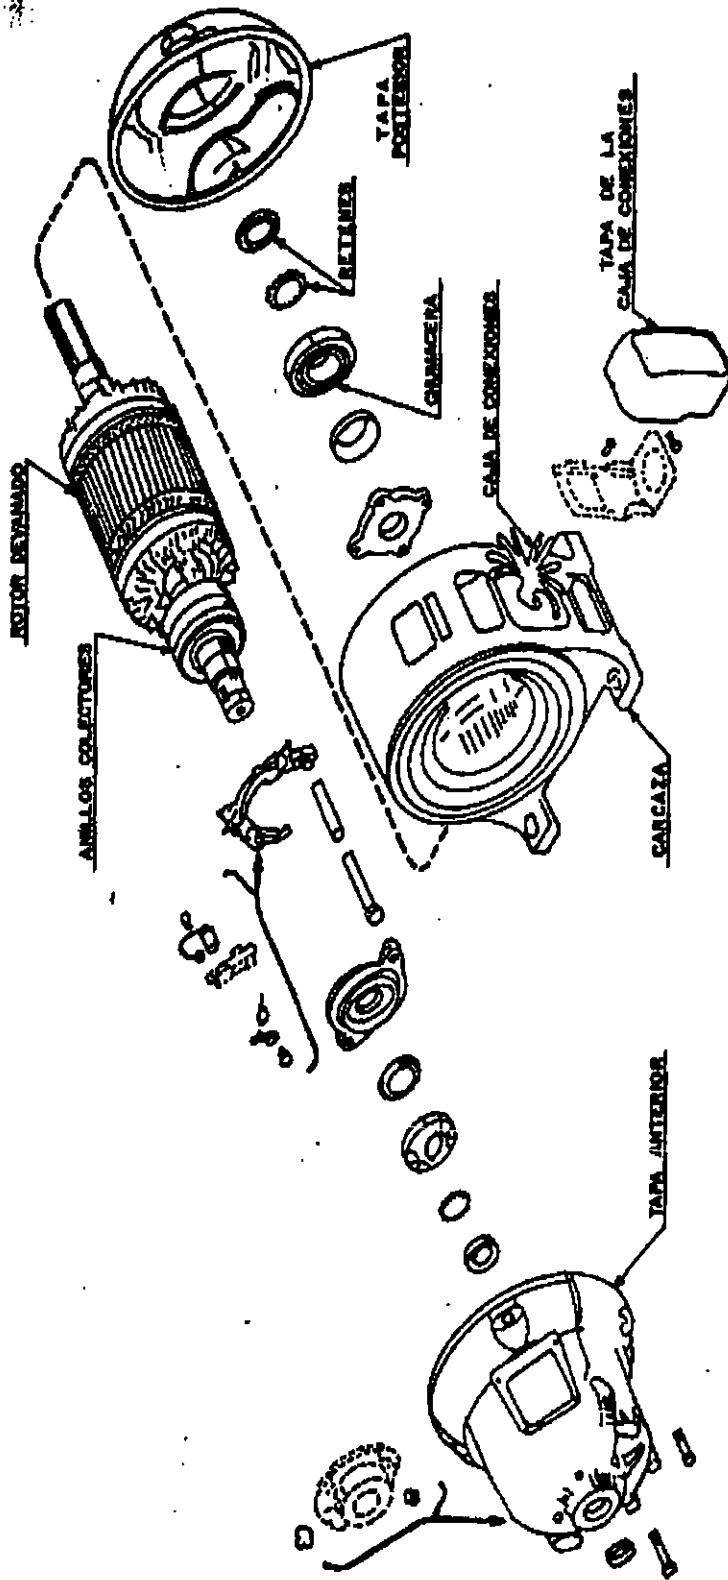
Vista de los principales componentes de un motor de inducción. Esta figura fue obtenida del libro de "El ABC De Las Máquinas Eléctricas II (Motores de Corriente Alterna)" de Gilberto Enríquez Harper.
